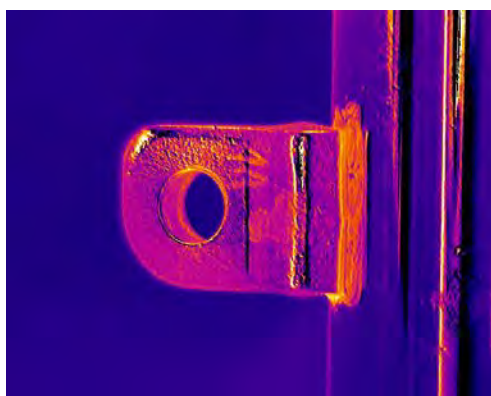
Snímací IR kamera<sup>18</sup>.
